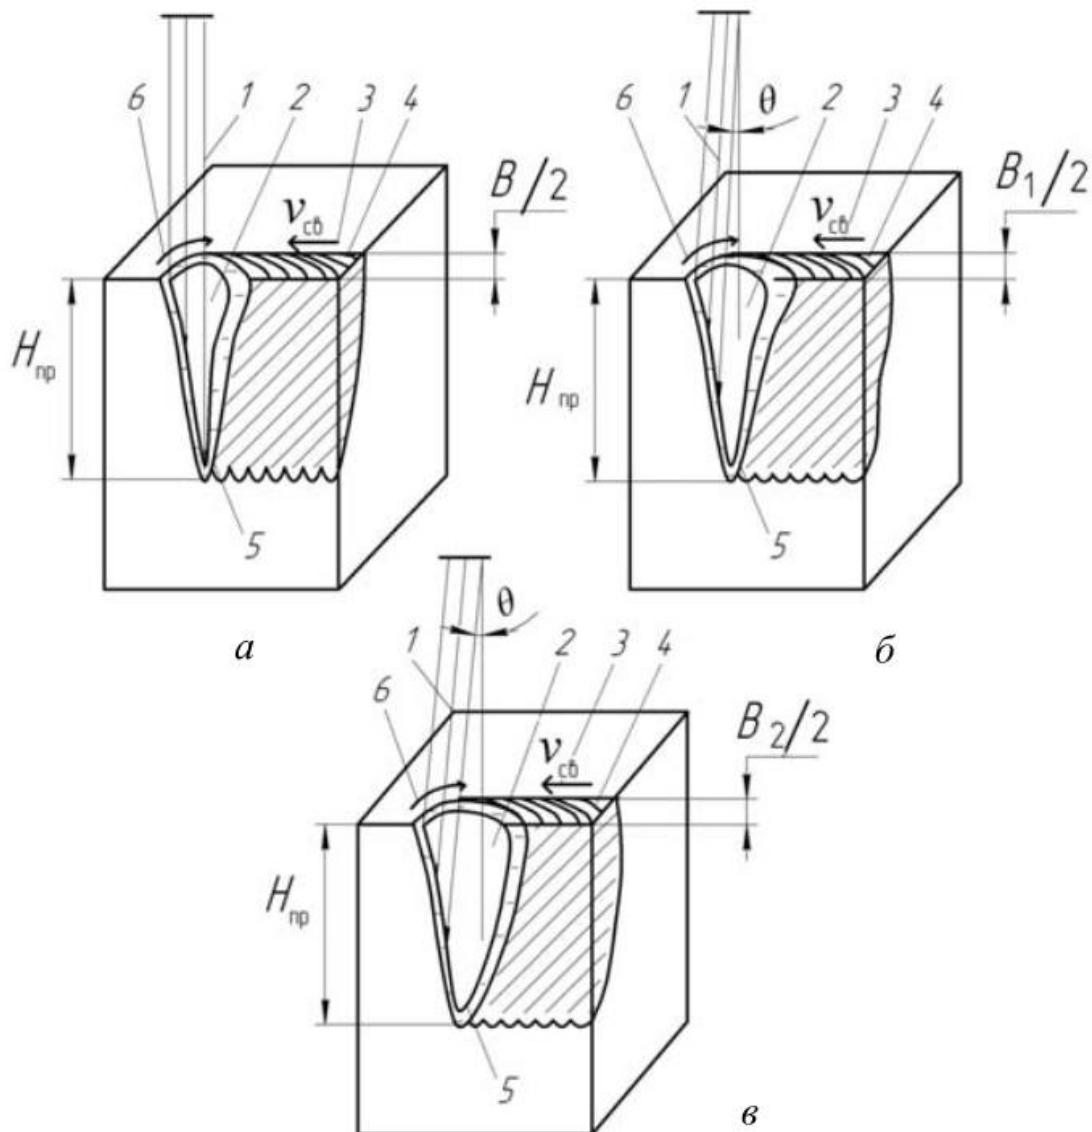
Схемы формирования металла шва при сварке неподвижным и сканирующим лучами:
